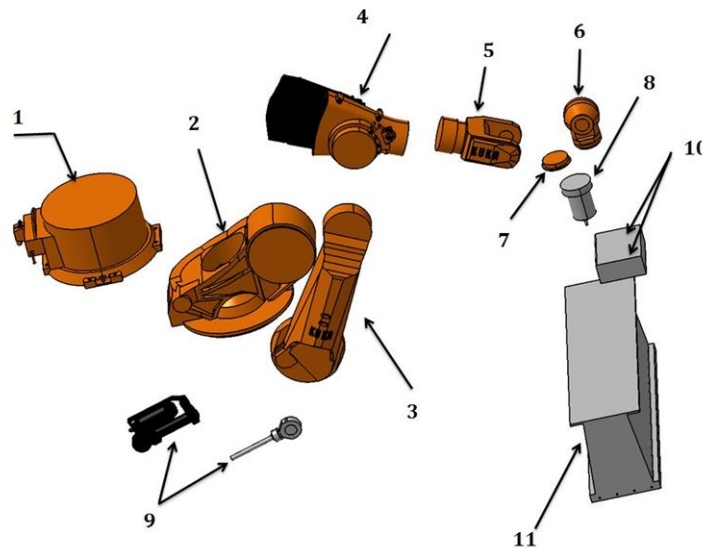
La Vue éclatée du robot industriel Kuka KR500-2MT
